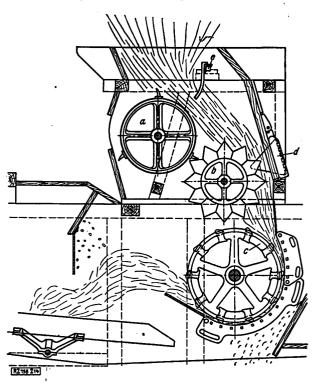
Selbsteinleger mit Strohschneider für Dreschmaschinen von Welger
